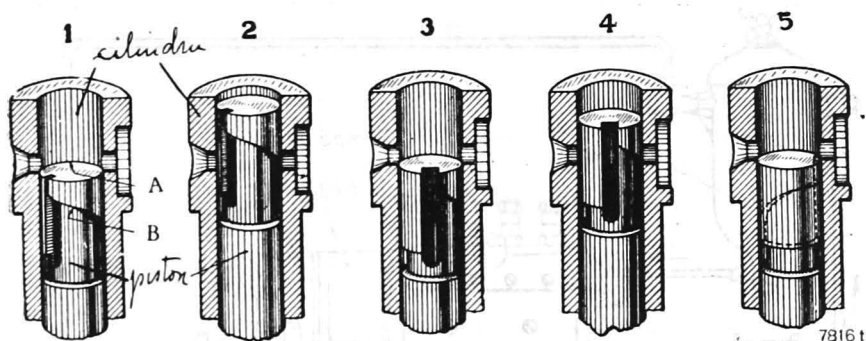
Secțiuni printr'un cilindru, arătând pistonul în diverse poziții de reglaj.
